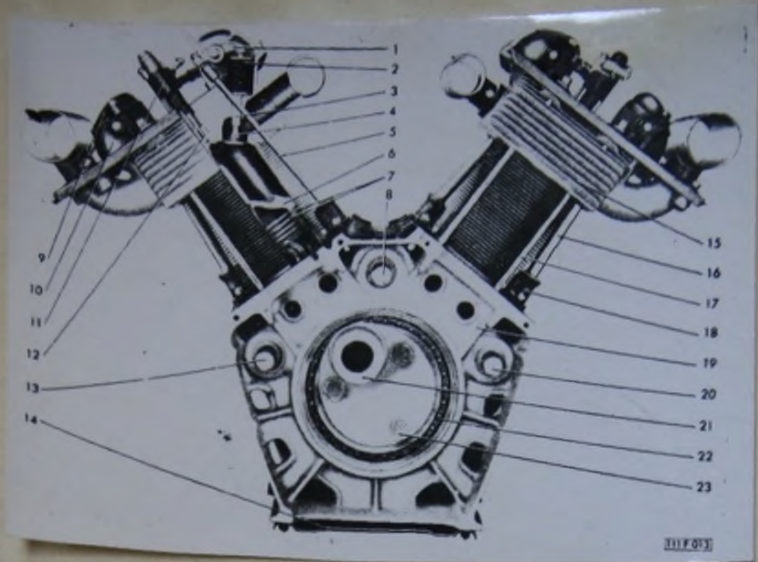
Двигатель автомобиля Татра III-R . Поперечный разрез.
